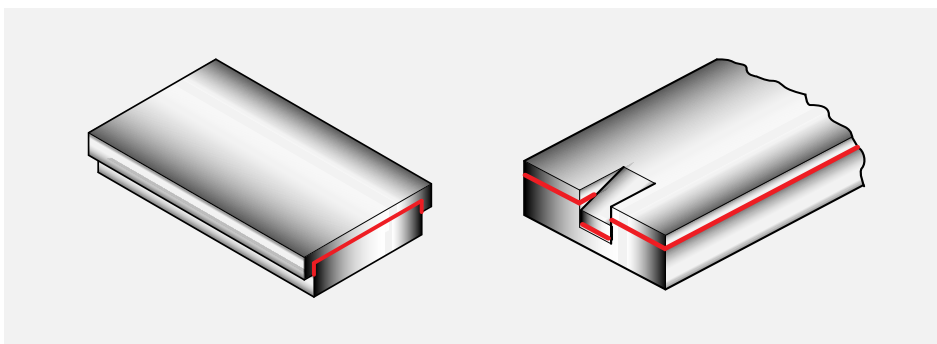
Fixação mecânica de placas de deslizamento DP4
